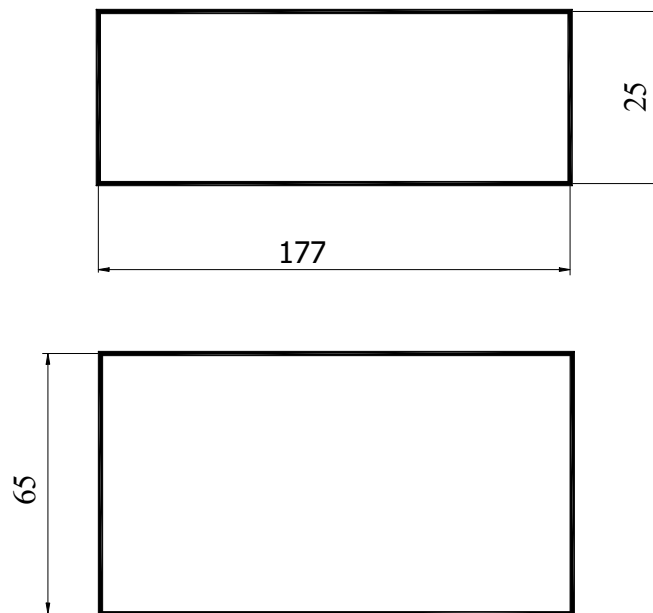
Ескіз заготовки із полосового прокату
